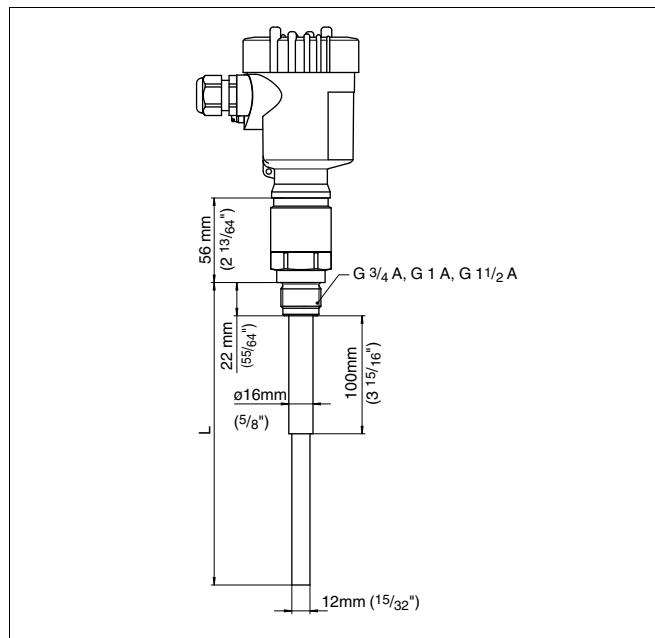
VEGACAL 62 - Резьбовое исполнение G1 A (ISO 228 T1)
